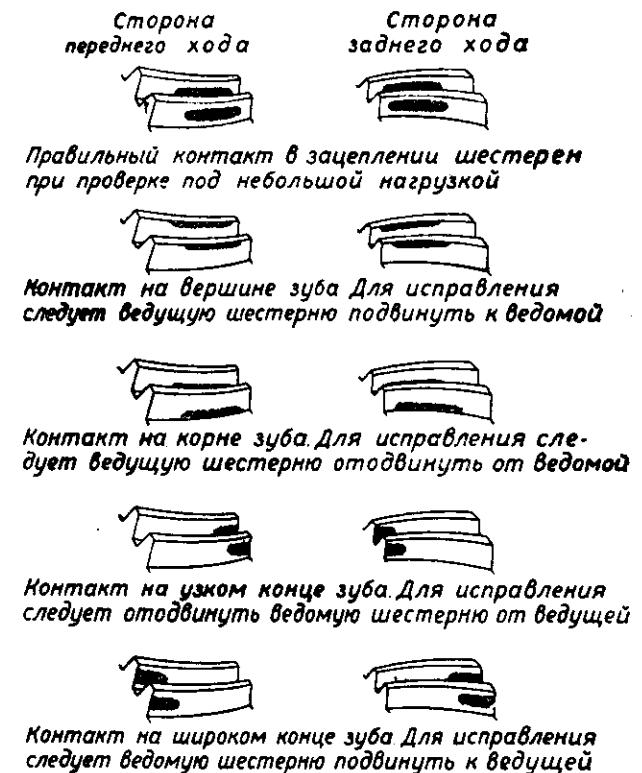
Пятьно контакта ведомой шестерни главной передачи
